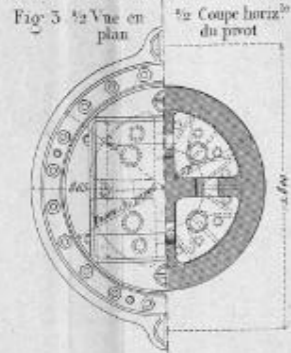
1/2 Vue en plan et 1/2 Coupe horiz. du pivot
